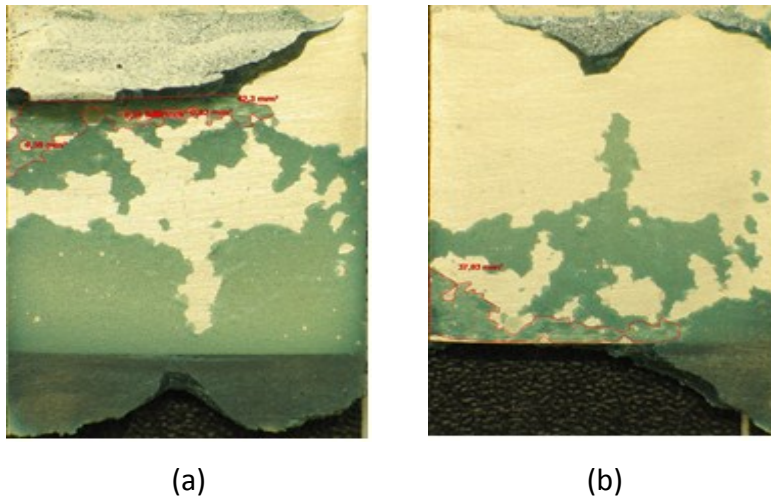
Provete 2 com "taper" em adesivo 30°. Superfície 1(a), Superfície 2 (b).
